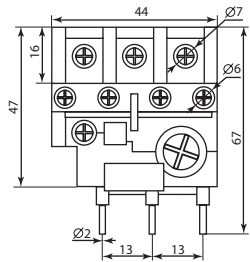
Габаритные и установочные размеры реле PTL-1001-M2...PTL-1022-M2
